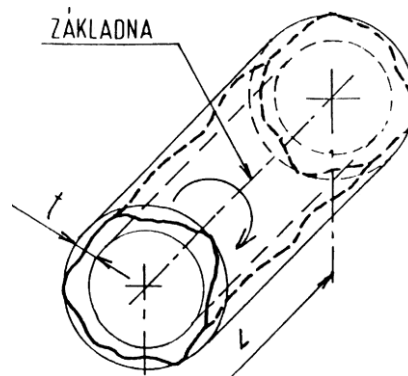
Vyobrazení tolerančního pole čelního kruhového házení [3]
